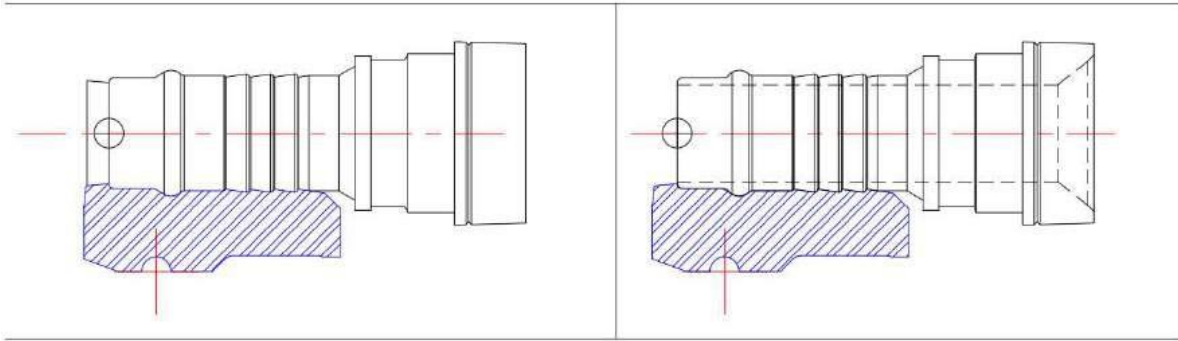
Perfil de inserto para acabado 3er Posición, físico vs teórico
